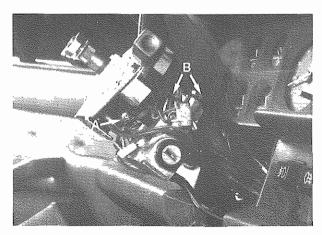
A - Viti fissaggio deviatore luci Switch block screws
